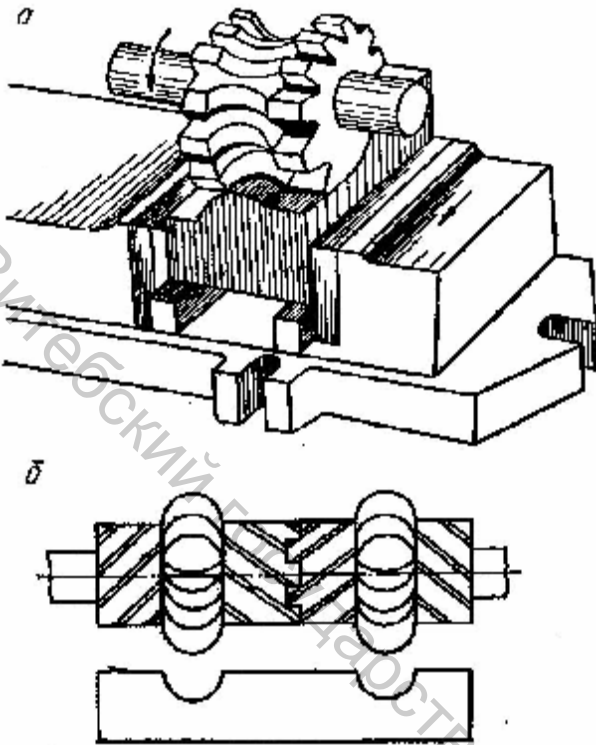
Фрезерование фасонных поверхностей фасонными фрезами
